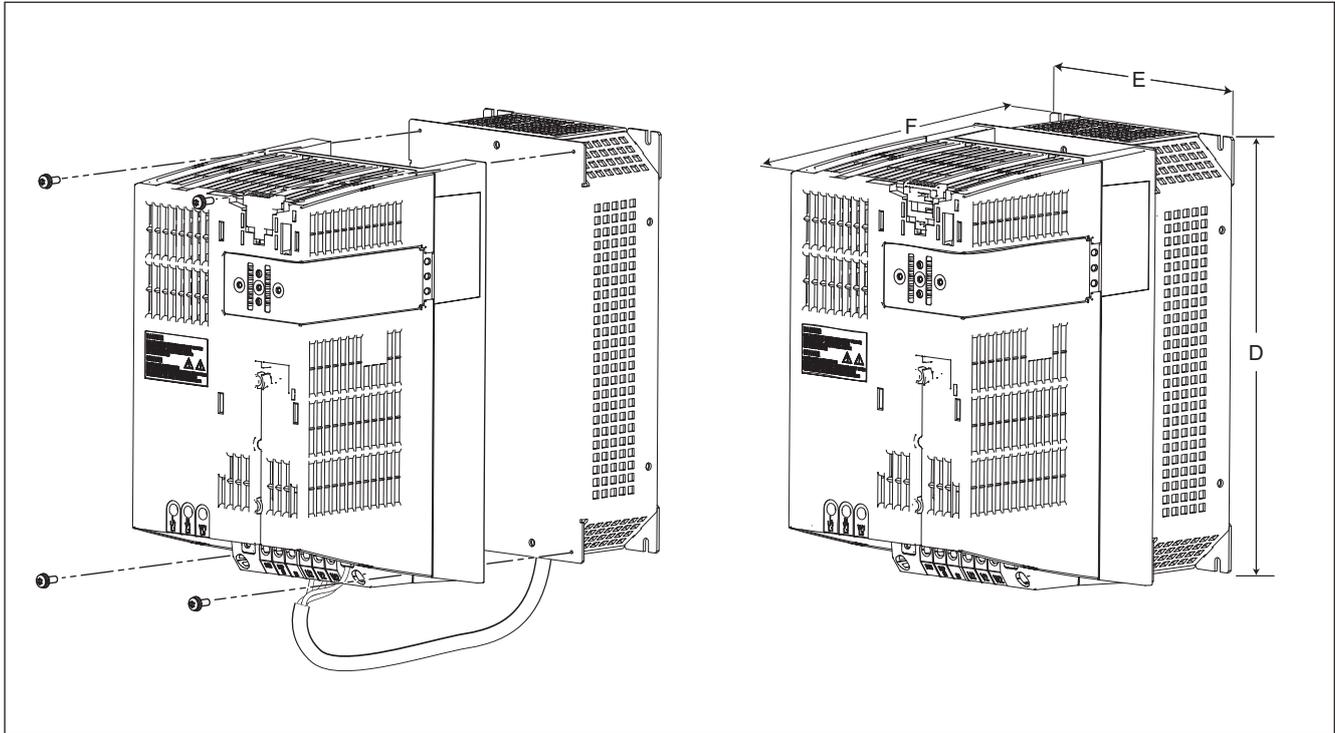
Montaggio di Power Module e bobina motore, grandezza costruttiva FSB e FSC
